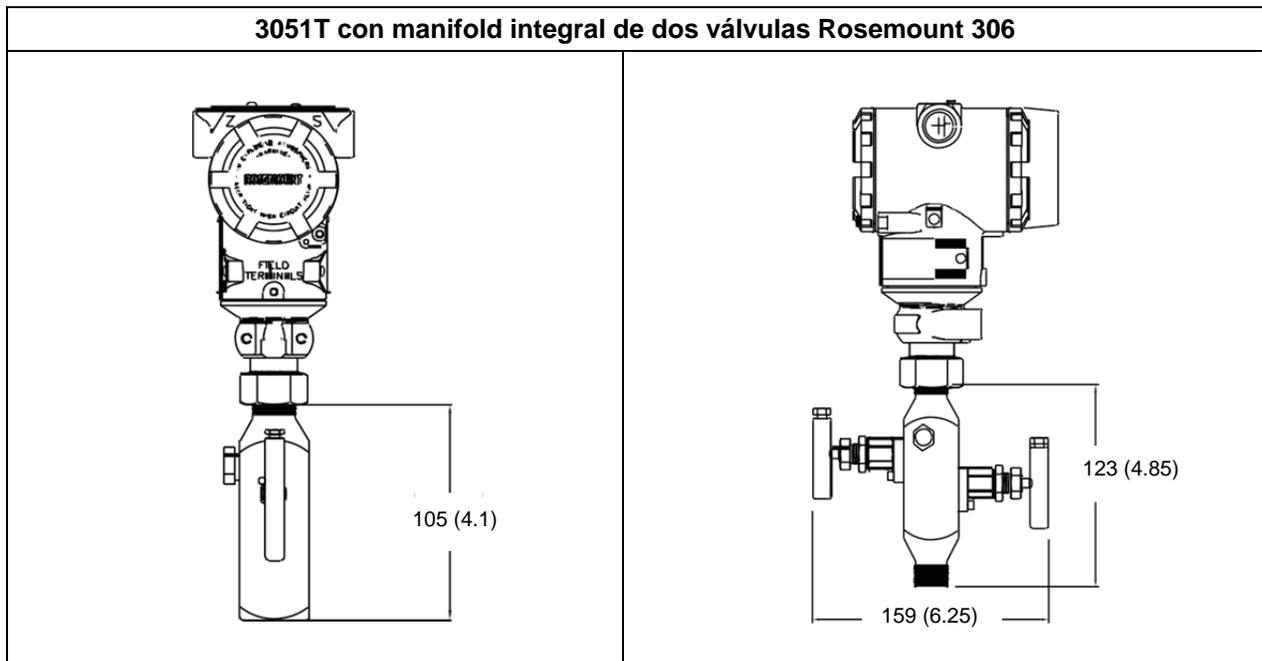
Dimensiones del transmisor Rosemount Modelo 3051T.
